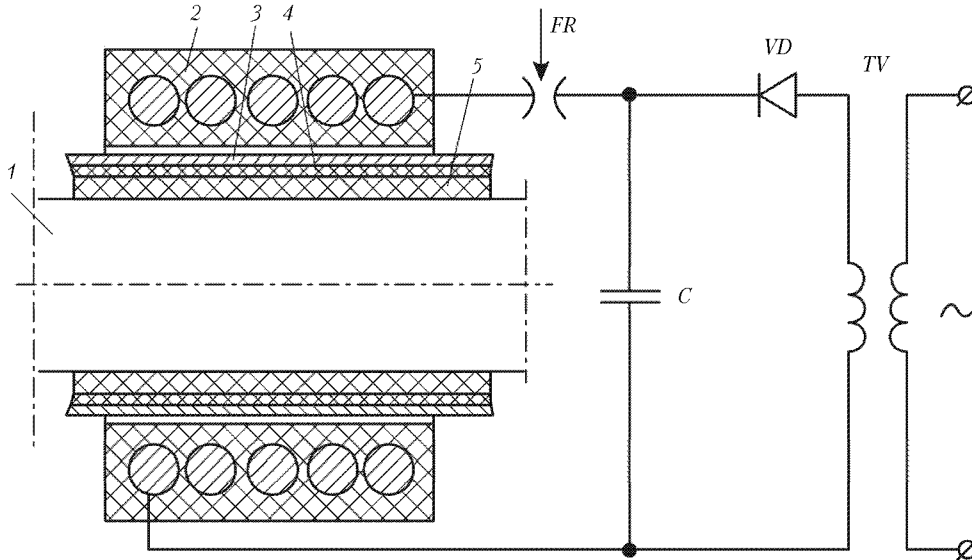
Схема устройства для магнитноимпульсного формования трубчатых стержней: 1 – оправка; 2 – магнитный индуктор (технологический инструмент); 3 – металлическая фольга (спутник); 4 – резиновая прослойка; 5 – полимерная труба; TV – повышающий трансформатор; C – батарея конденсаторов; VD – выпрямитель; FR – разрядник
